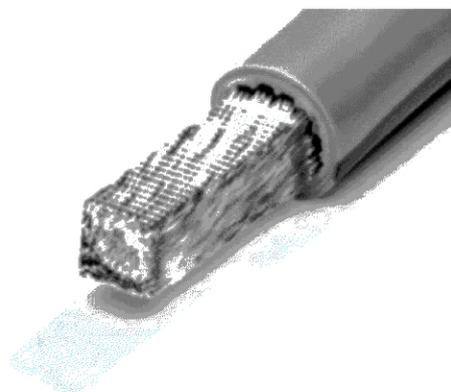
Односторонняя ультразвуковая сварка
